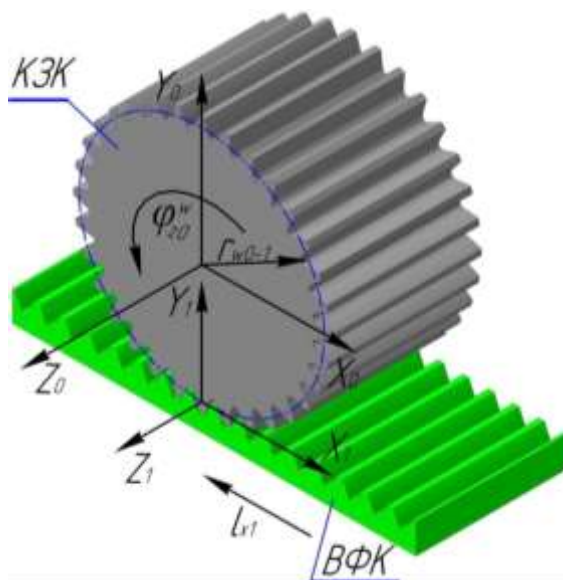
Кінематична схема оберненого теоретичного формоутворення прямозубого циліндричного зубчастого колеса
